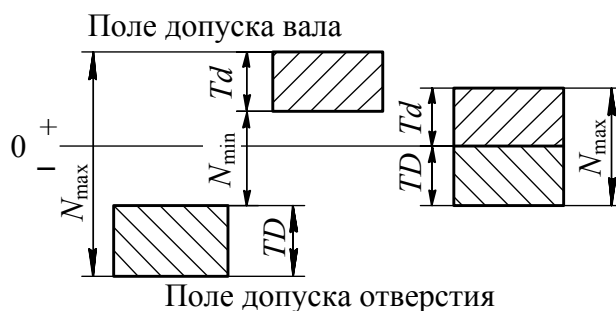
Схема расположения полей допусков для посадок с натягом
